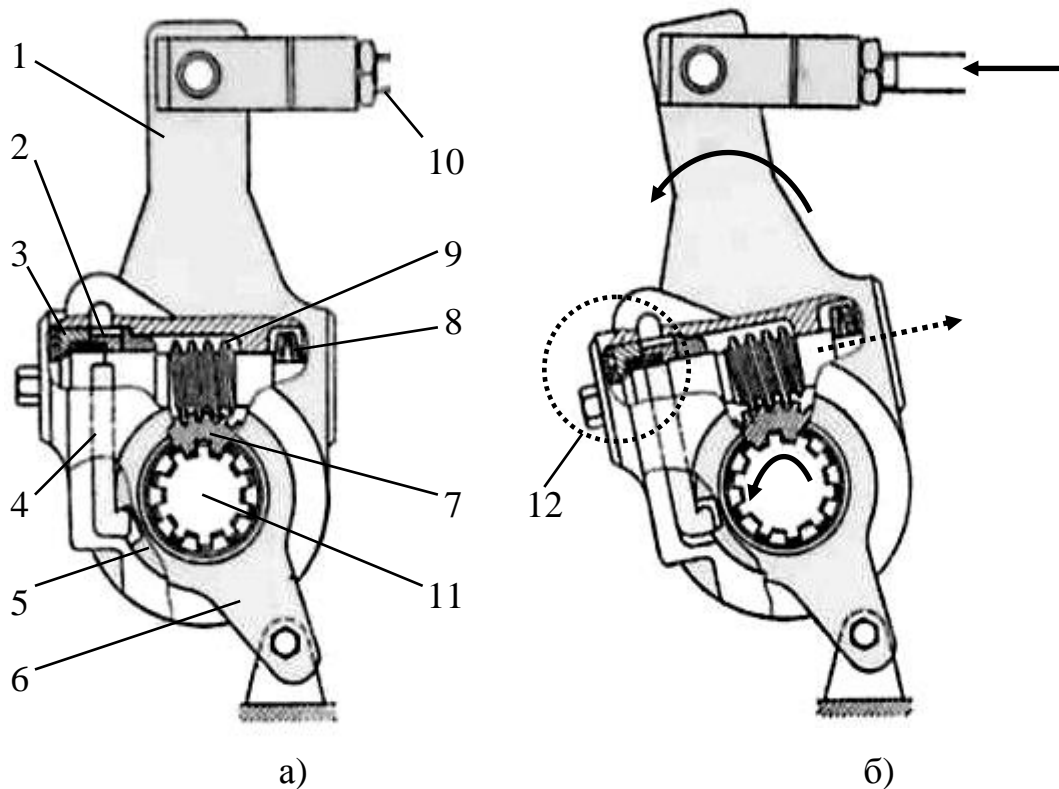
Устройство автоматической регулировки зазора между тормозными колодками и барабаном тормозного механизма автомобиля КАМАЗ-6460: а – торможения нет, б – торможение; 1 – корпус рычага регулировочного устройства; 2 – шестерня; 3 – полу-муфта наружная; 4 – зубчатая рейка; 5 – диск; 6 – неподвижный рычаг; 7 – червячное зубчатое колесо; 8 – пружина; 9 – вал с червяком; 10 – шток тормозной камеры; 11 – вал кулачка разжимного устройства тормозного механизма; 12 – подробнее см. на рис. 2.23
